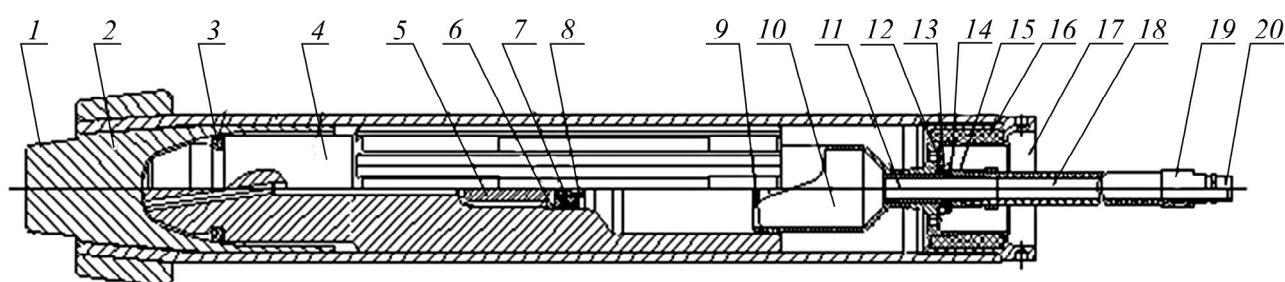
Конструкция пневмомолота “Тайфун”: 1 — корпус; 2 — наковальня; 3 — резиновое кольцо; 4 — ударник; 5 — инерционный клапан; 6 — упорное кольцо; 7 — резиновое седло; 8 — жиклер; 9 — полиэтиленовое кольцо; 10 — патрубок; 11 — стемель; 12 — ступица; 13 — клапан; 14 — стальное кольцо; 15 — гайка; 16 — демпфер; 17 — хвостовик; 18 — рукав; 19 — гайка; 20 — штуцер
